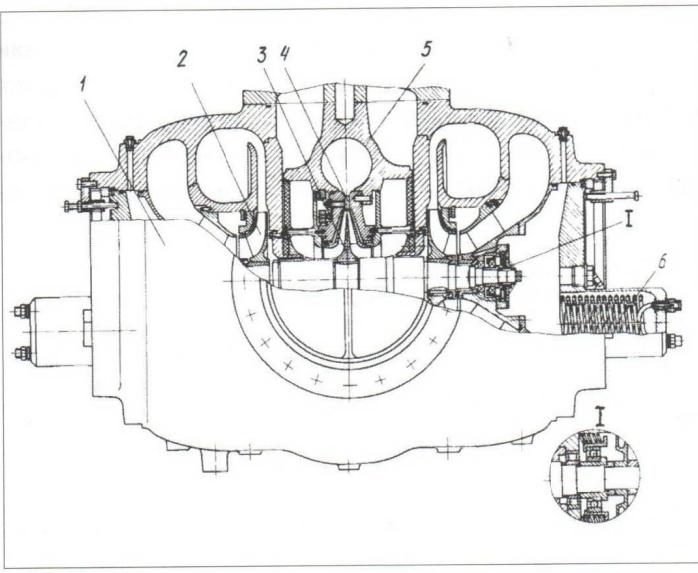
Детандер-компрессорный турбоагрегат ТКО-75/42:
